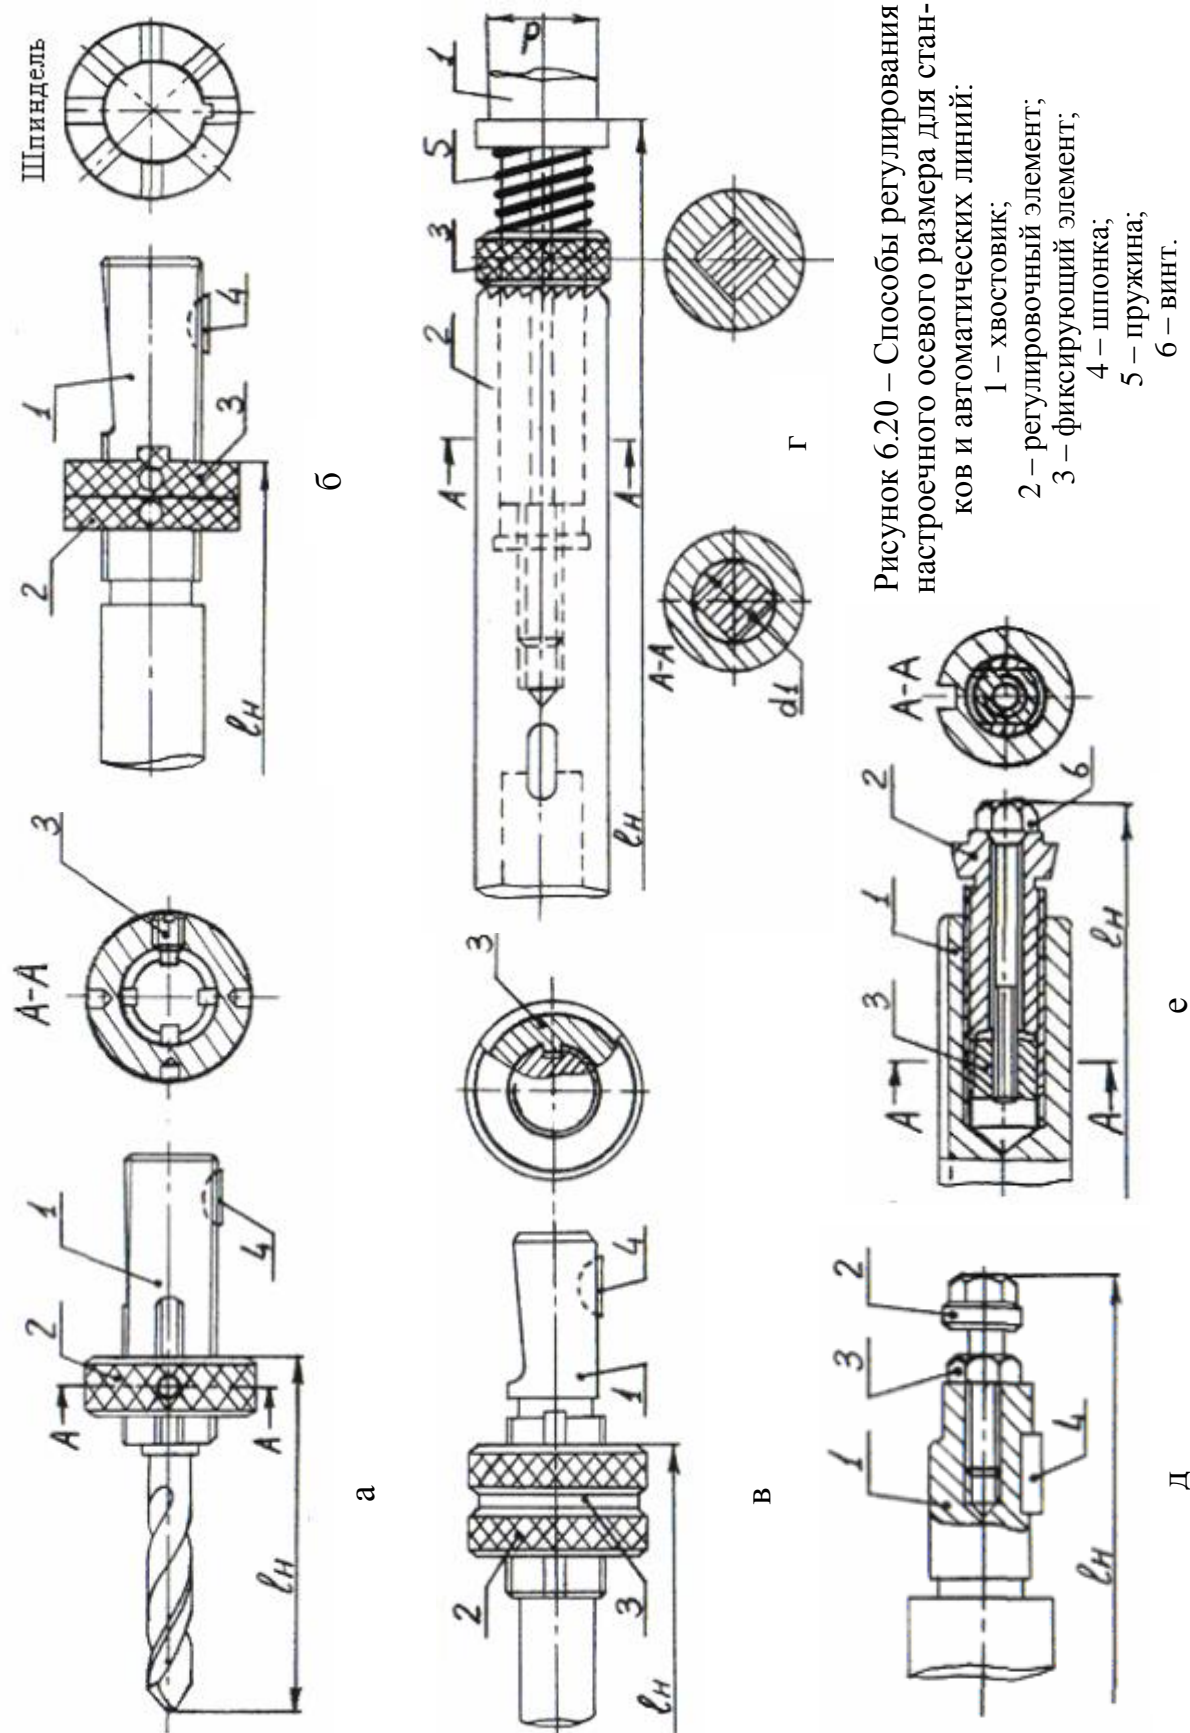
Способы регулирования настроенного осевого размера для станков и автоматических линий:
